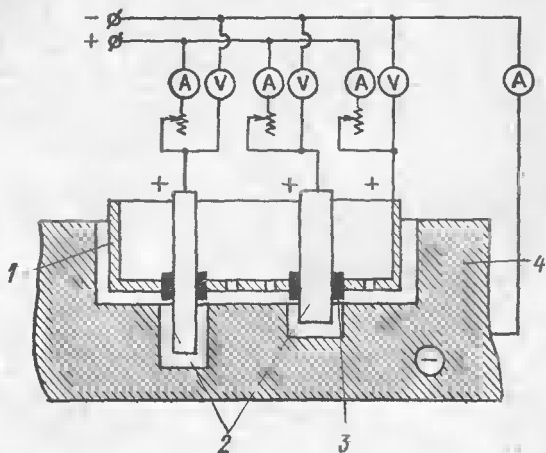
Схема приспособления для хромирования деталей с глубоким рельефом:
